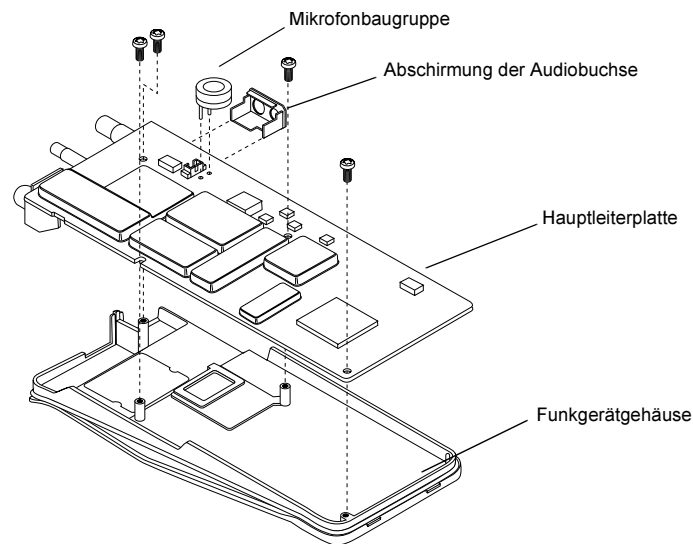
Entfernen der Hauptleiterplatte vom Gehäuse
